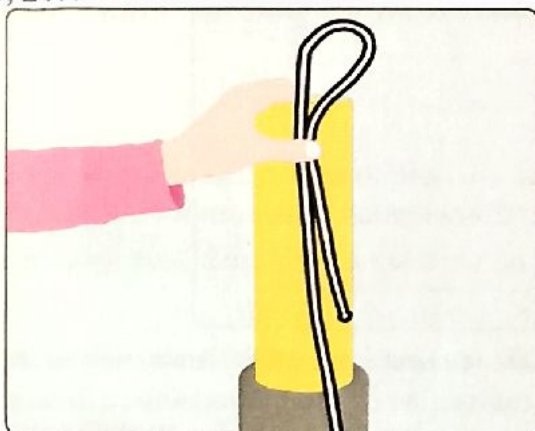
Подготовка втулки к проворачиванию при помощи веревки со свободными концами – 1-й этап
